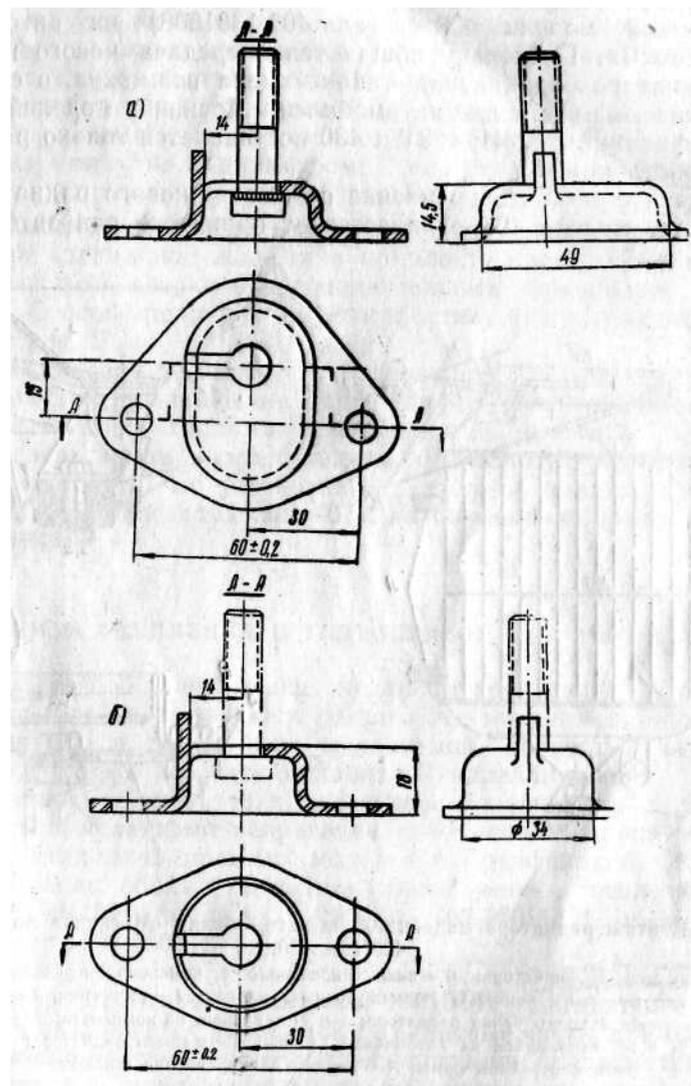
Переходная деталь узла крепления передней опоры двигателя:
